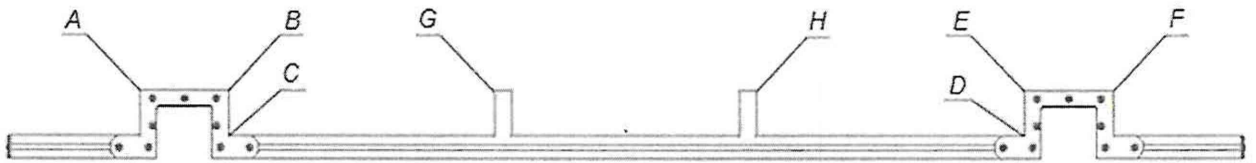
Общий вид калибровочных линеек ВО-00.211-01 и ВО-00.211-03 с контрольными точками;
